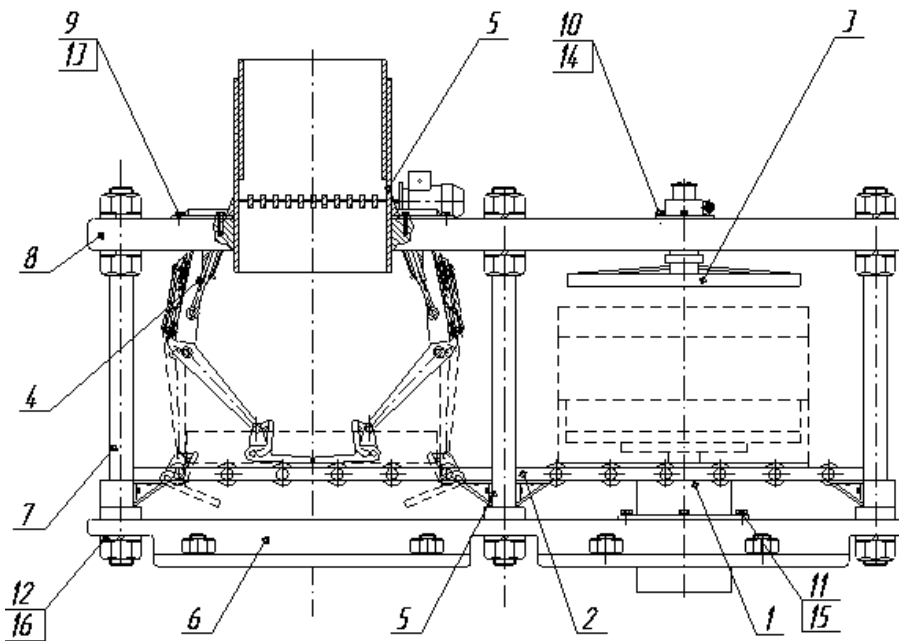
Схема формовочной машины с двухсторонним прессованием:
